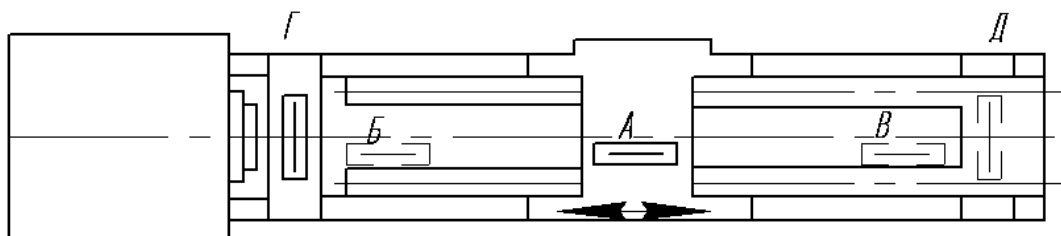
Схема проверки точности направляющих станины станка
